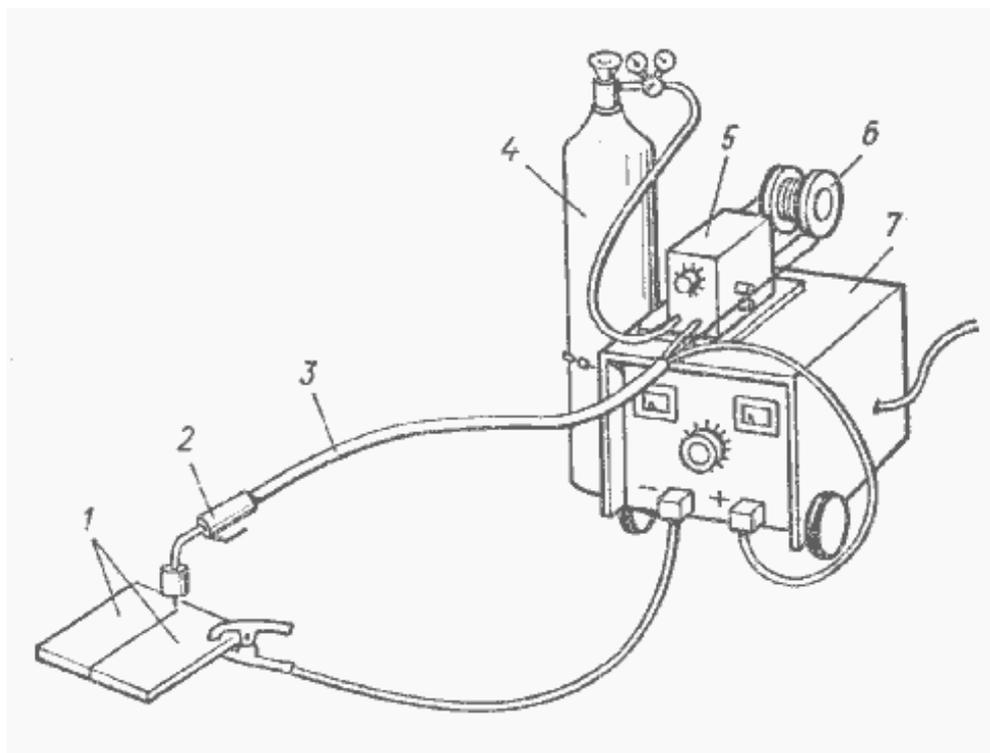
Сварочный пост полуавтоматической дуговой сварки в среде аргона
